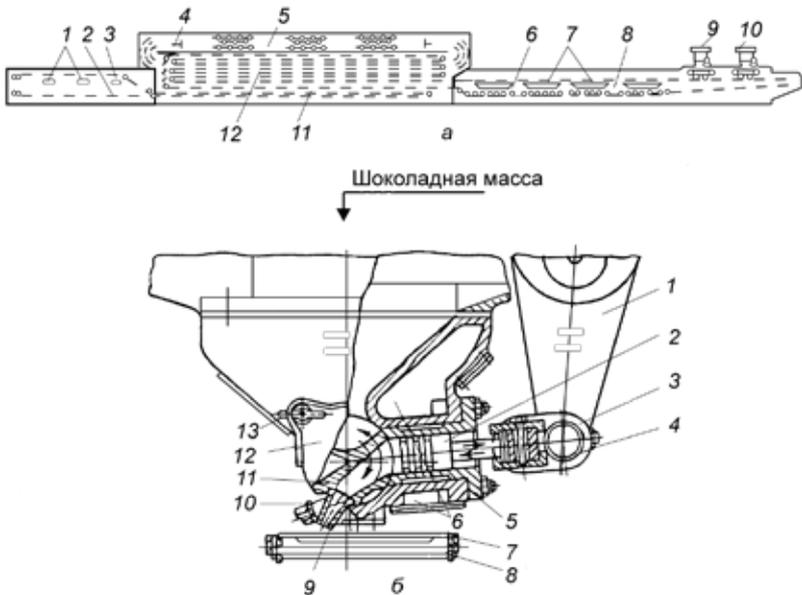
Агрегат для формования плиточного шоколада с двумя отливочными машинами:
